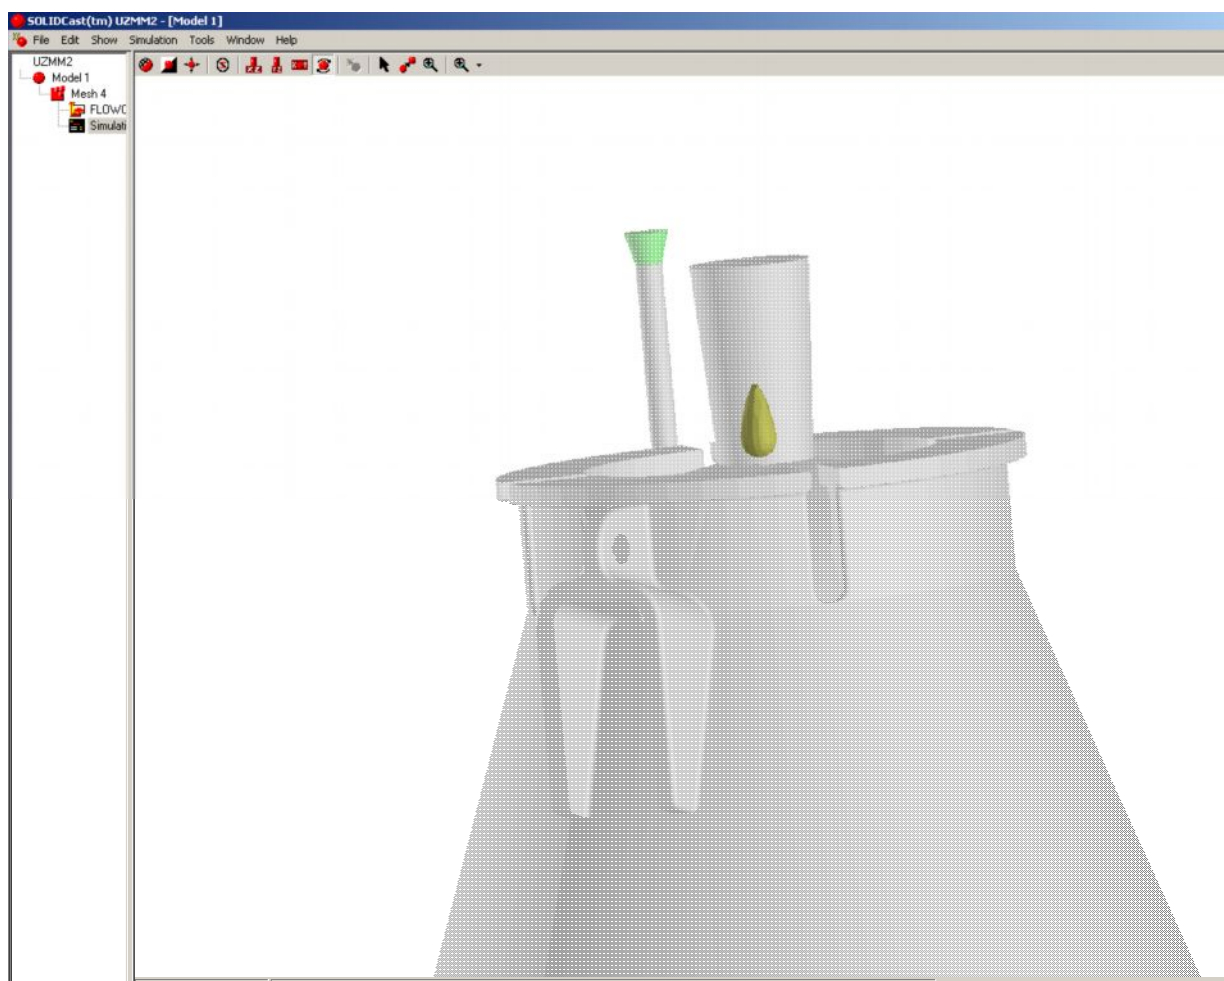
Усадочные дефекты в отливке “Чаша”
